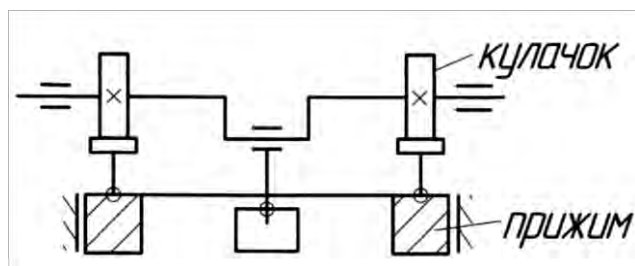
Схема вытяжного прессы двойного действия с кулачковыми парами
